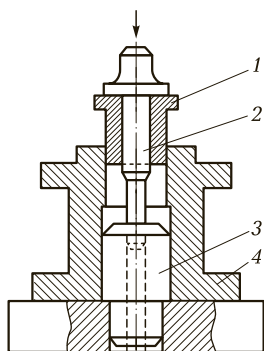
Приспособление для центрирования втулки относительно корпуса:
